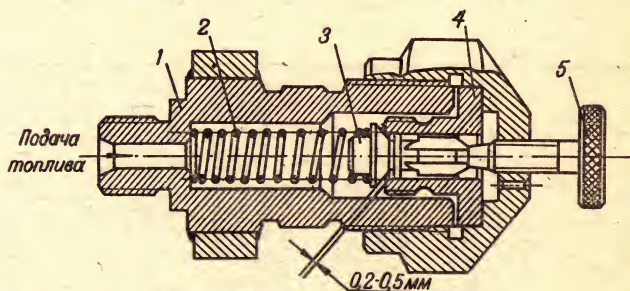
Проверка гидравлической плотности обратного клапана с седлом на приспособлении к прибору КИ-562:
